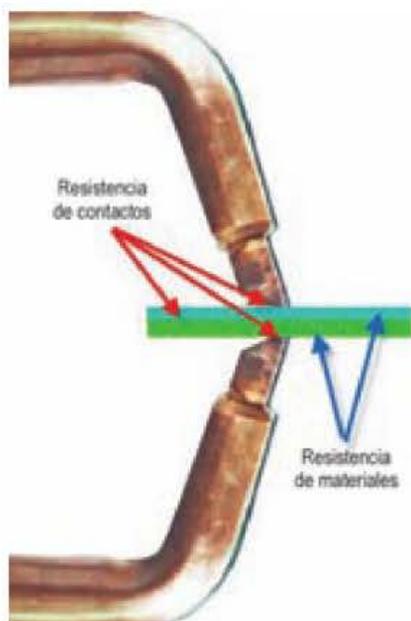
Resistencias en un punto de soldadura.
